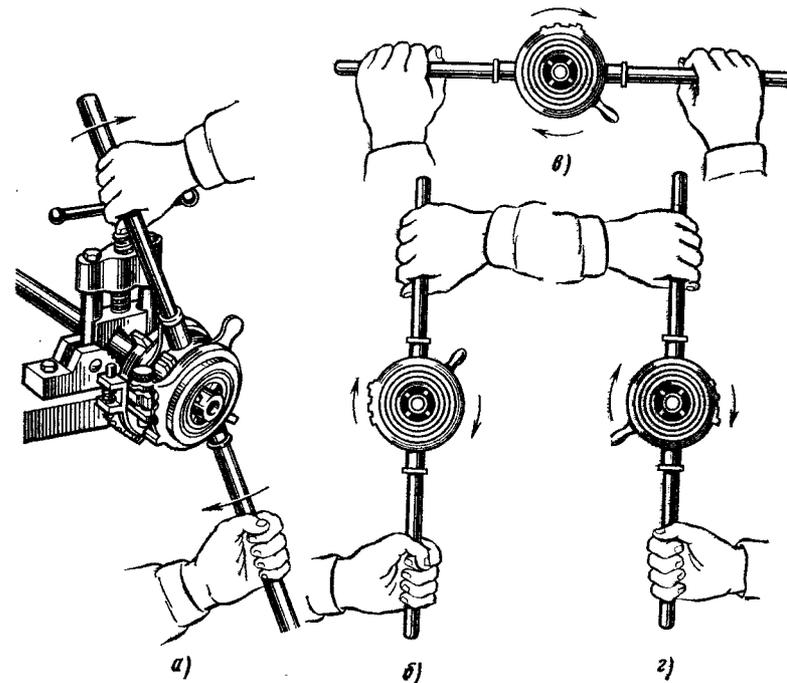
Нарезание трубной резьбы клуппом: а — общий вид; б — первый поворот; в — второй поворот; г — третий поворот
